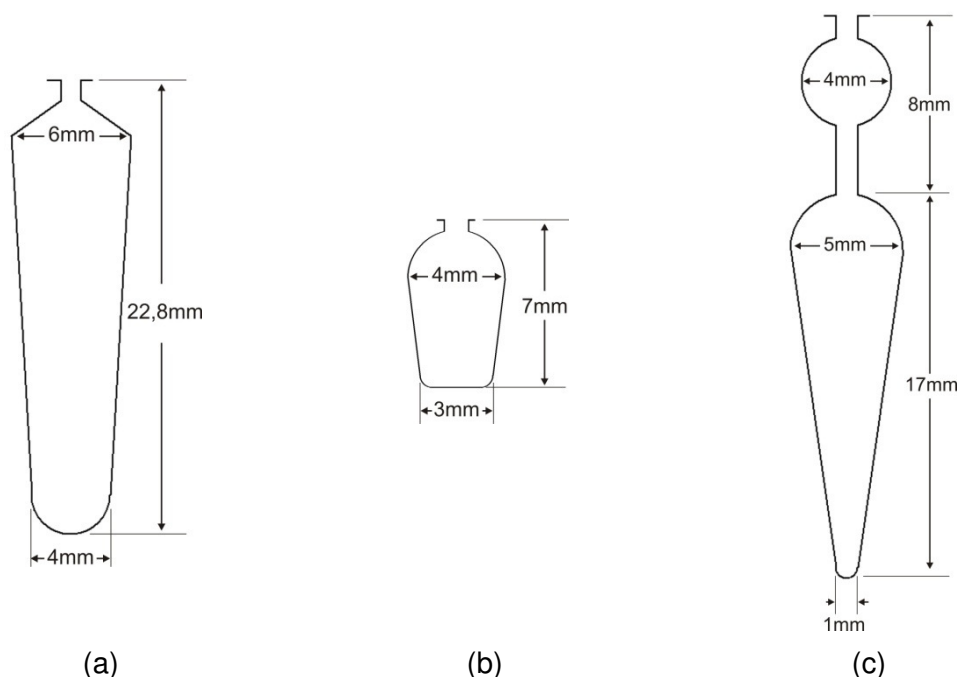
Dimensões das ranhuras: (a) Motor 1 ; (b) Motor 2 ; (c) Motor 3.
